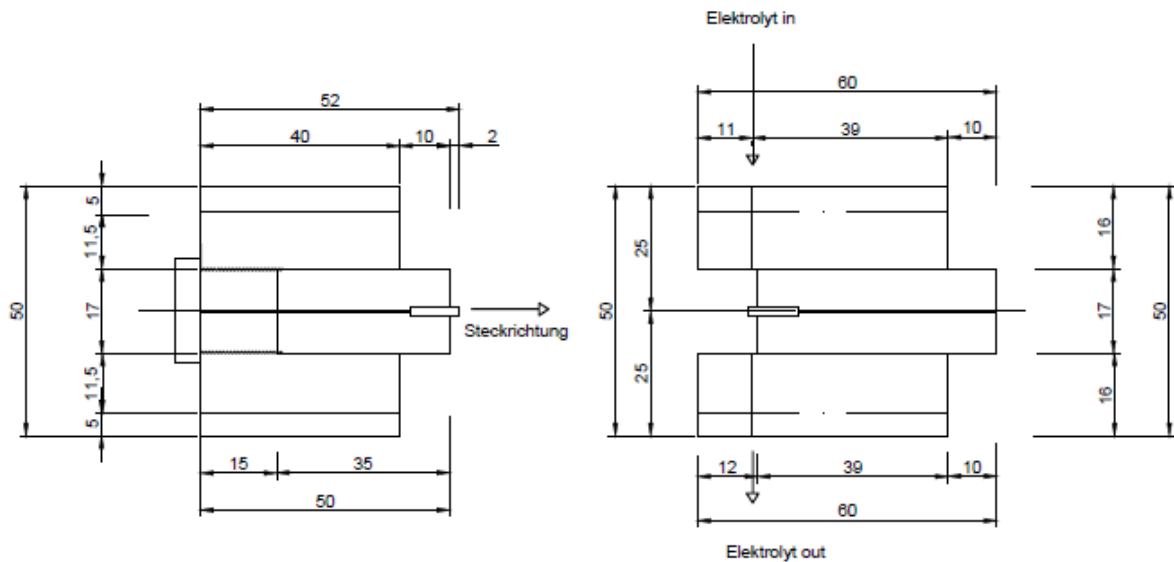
Grundriss der konstruierten Zelle, erstellt mit AutoCAD.
